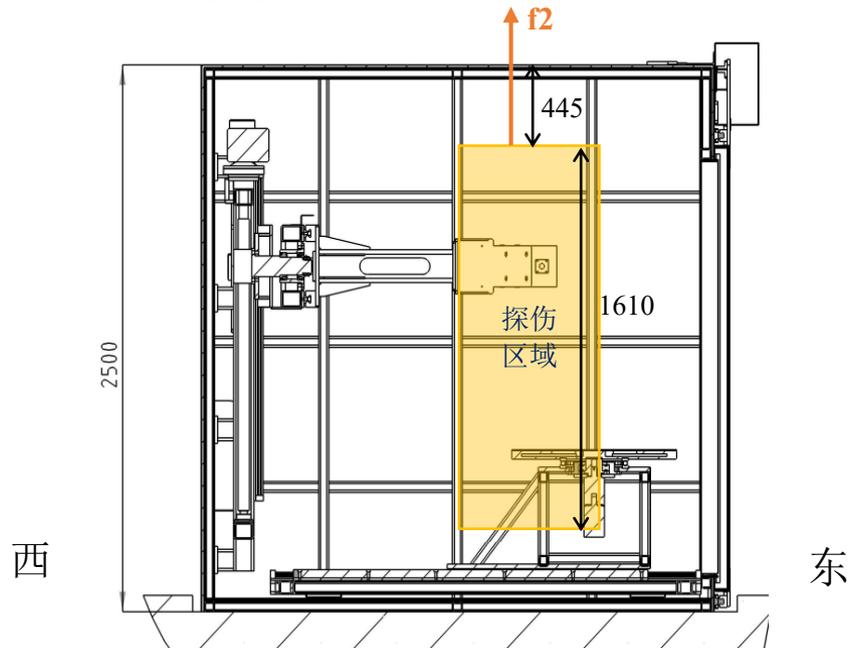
辐射屏蔽计算预测点位剖面图（永久路厂区）（单位：mm）
